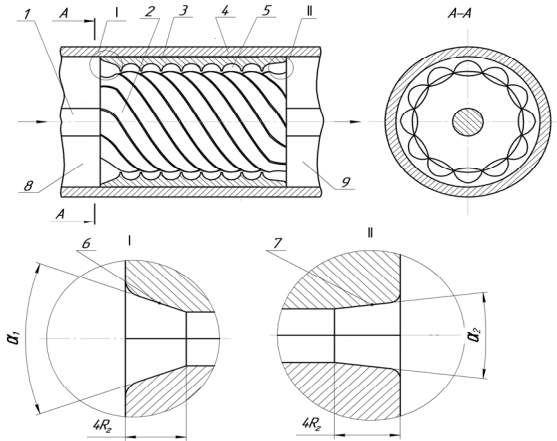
Удосконалені робочі органи насоса [7]: 1 – привідний вал; 2 – гвинт; 3 – втулка; 4 – корпус; 5 – гвинтова канавка; 6 – вхід в робочу зону ЛГН; 7 – вихід з робочої зони ЛГН; 8 – камера підводу; 9 – камера відводу.
